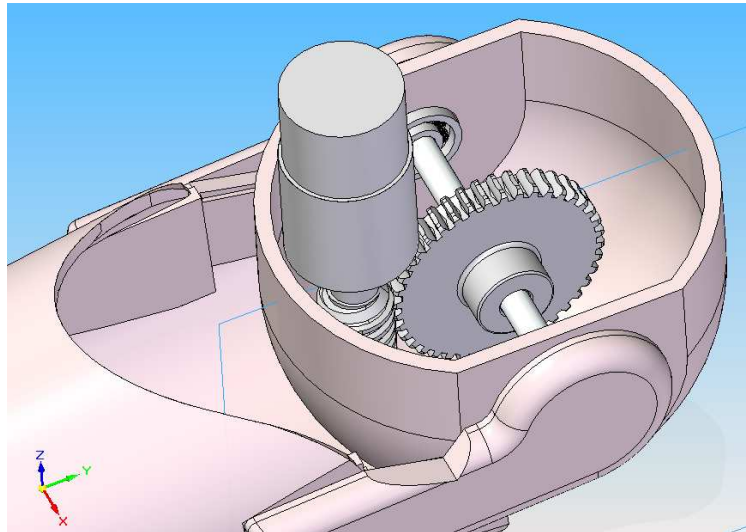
Mecanismo tornillo sinfín ensamblado al soporte
